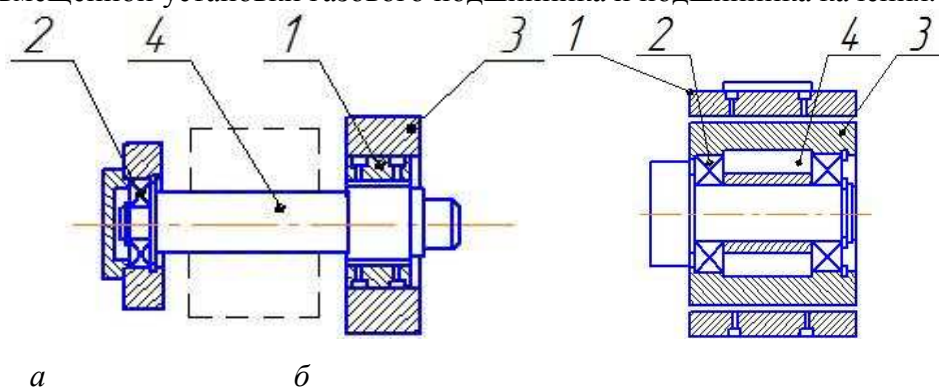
Схемы совмещенной установки газового подшипника и подшипника качения; 1- газовый подшипник; 2 - подшипник качения; 3 - корпус , 4-шпиндель: а- раздельная; б - параллельная
